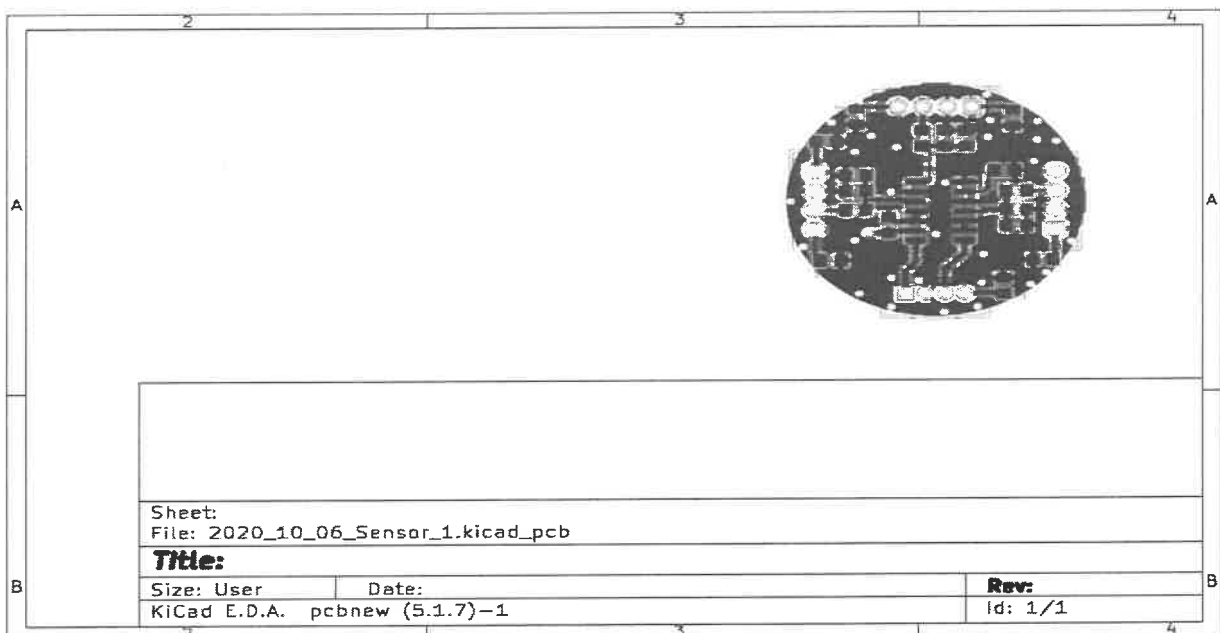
Projekt płytki PCB układu wejściowego front-end dla sensora 3-elektrodowego.
